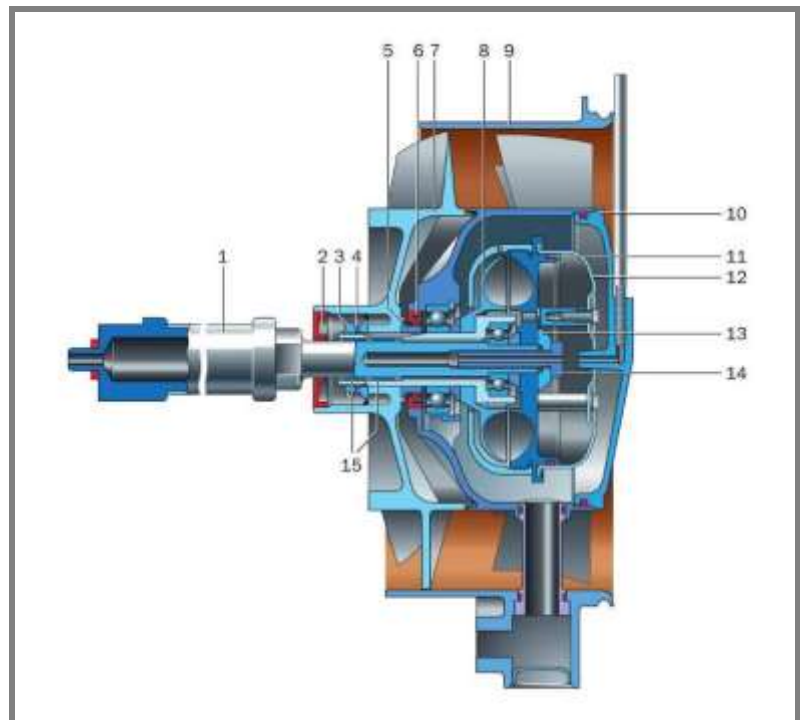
Установка гідравлічної муфти в приводі вентилятора: 1 – вал приводу вентилятора; 2, 6 – сальники (манжети); 3 – гайка вала; 4 – стопорна шайба; 5 – втулка сальника; 7 – робоче колесо; 8 – гідромуфта; 9 – корпус вентилятора; 10 – кришка; 11 – кільце ущільнювача; 12 – корпус центрифуги; 13 – шайба; 14 – маслопроводний болт; 15 – підшипник ковзання
